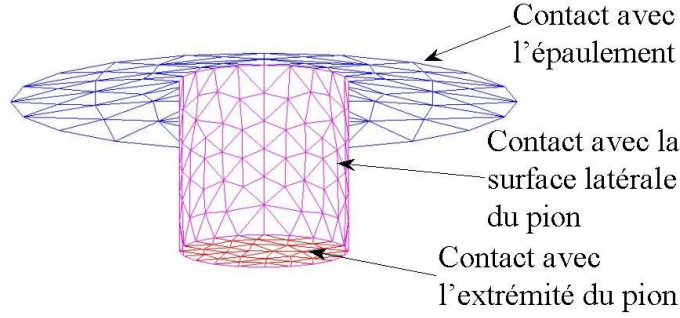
Surfaces de contact entre l'outil et la matière.
